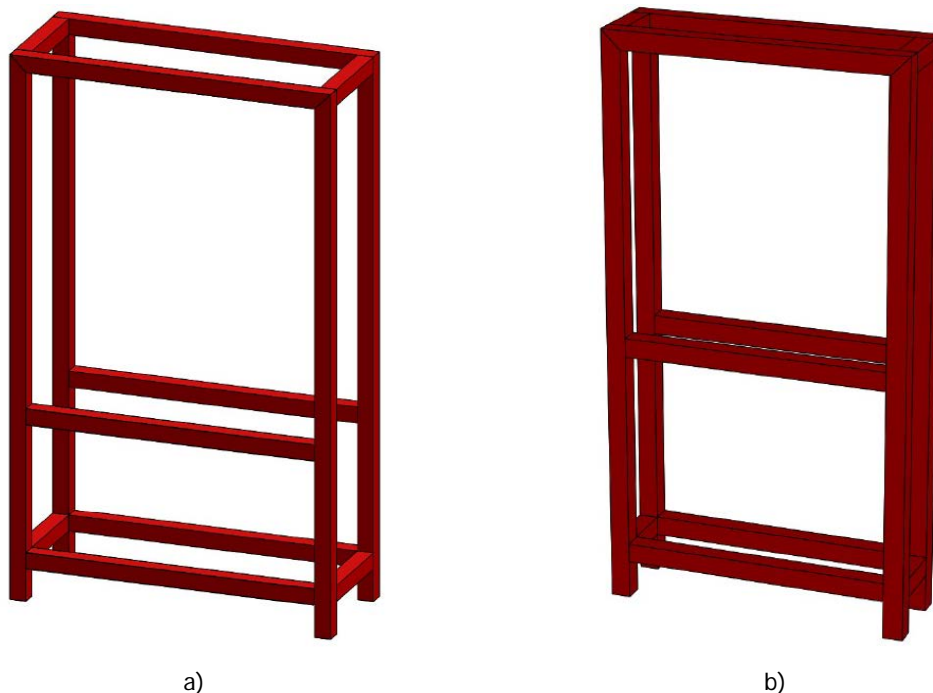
Estruturas de apoio: a) para tubeira divergente; b) para o estator de estabilização.
